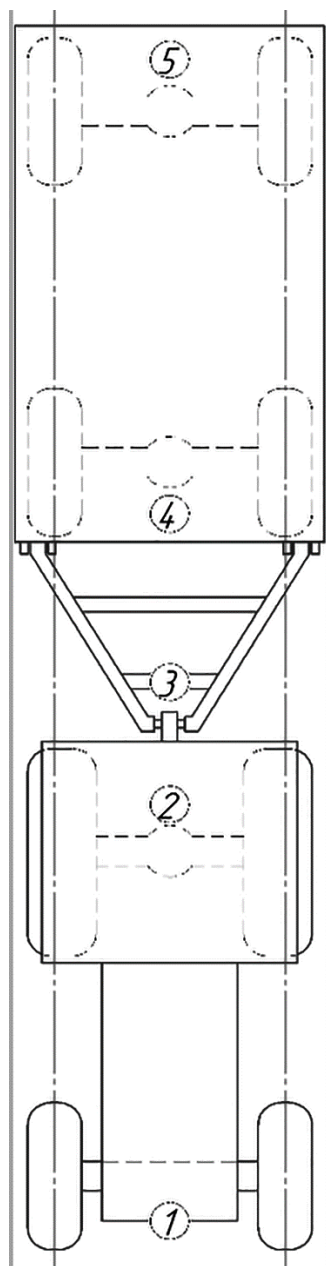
Точки установки датчиков считывающего приборного комплекса
